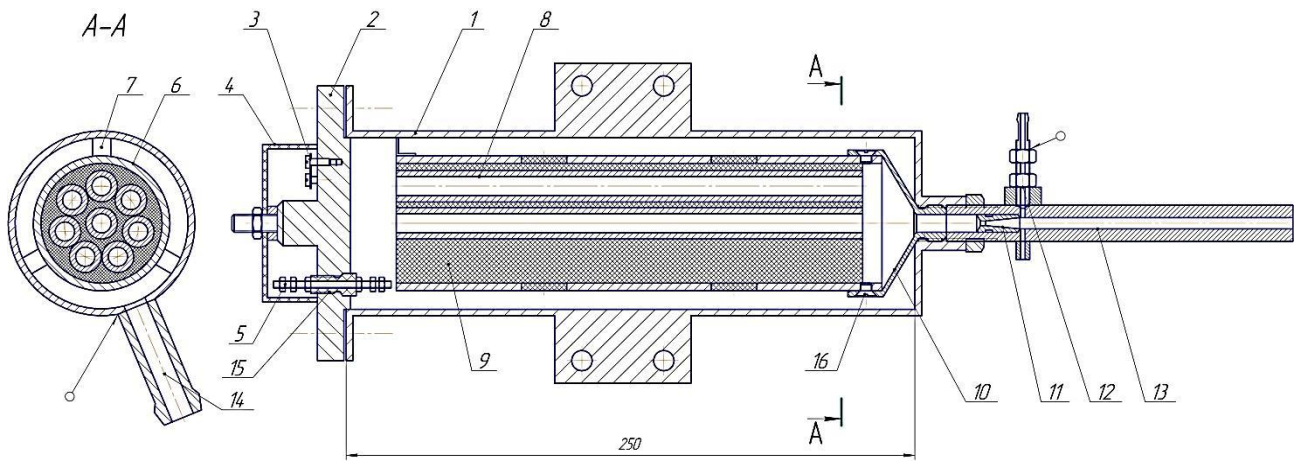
Схема газодинамічного напилювального пристрою.
